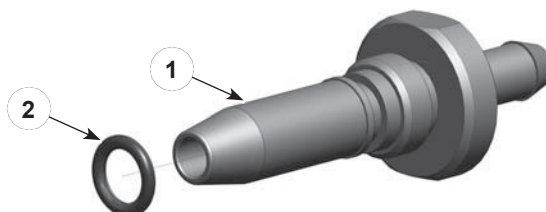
Kit d'assemblage de l' de l'adaptateur
